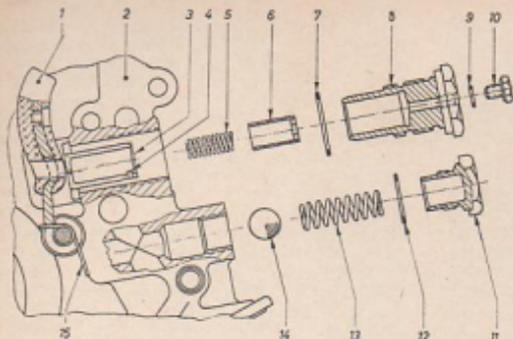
Oldruckkolben mit Feder in Drucksegment einführen
